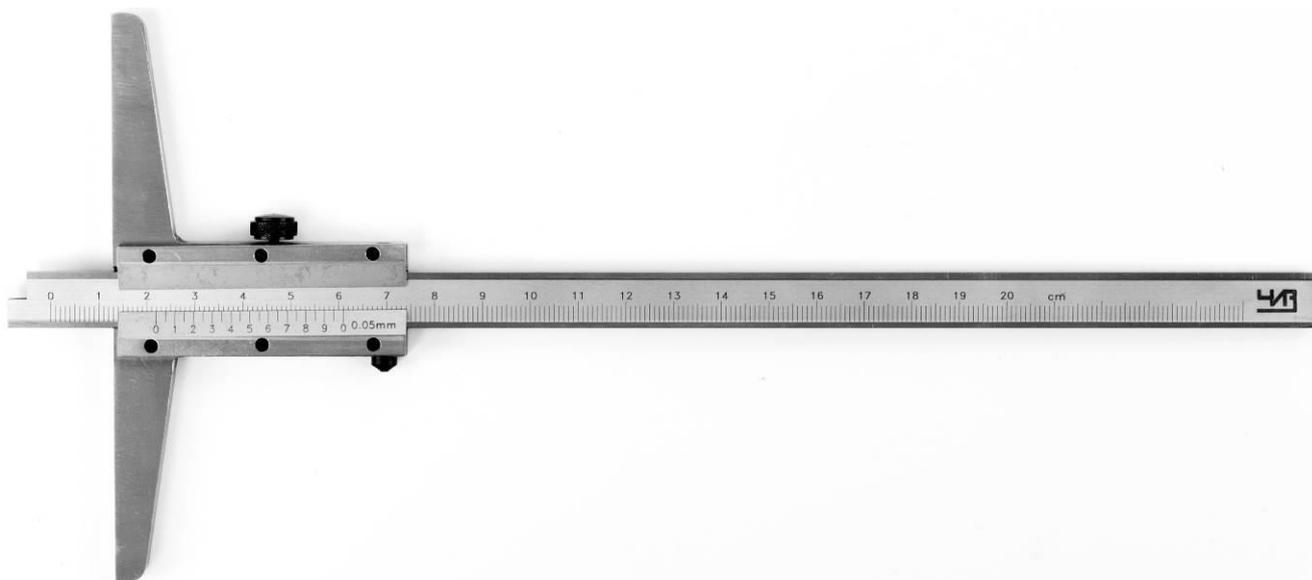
Общий вид штангенглубиномеров модификации ШГ со ступенчатым торцом штанги
